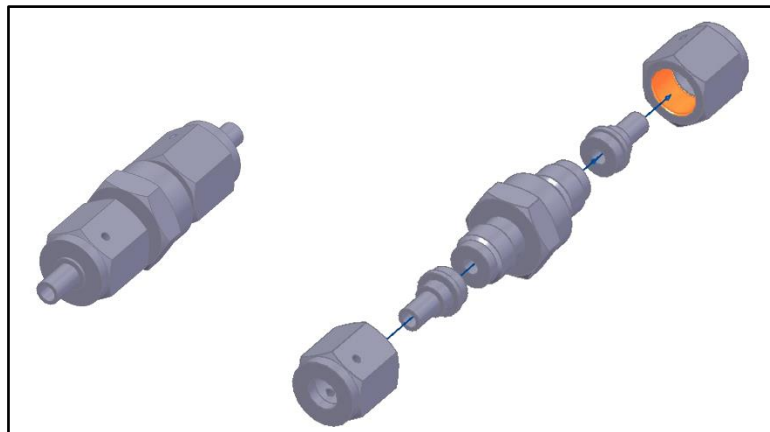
Válvula de retenção com as ligações VCR® montadas (esq.) e em vista explodida (dir.).
